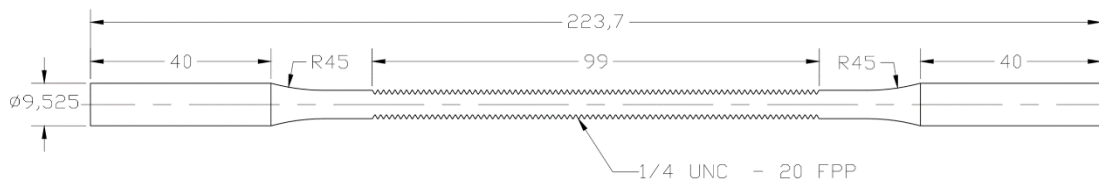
Dispositivo de teste para os tirantes, dimensões em milímetros, exceto a rosca.
